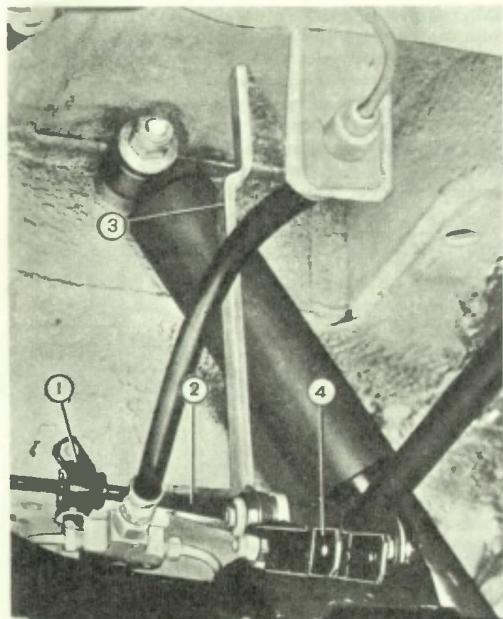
Установка приспособления А.72245 (или 67.7820-9518) для регулировки положения регулятора давления задних тормозов: 1 — кронштейн рычага привода регулятора давления; 2 — рычаг привода регулятора давления; 3 — приспособление А.72245 (или 67.7820-9518); 4 — тяга, соединяющая рычаг привода регулятора давления с кронштейном балки заднего моста.
